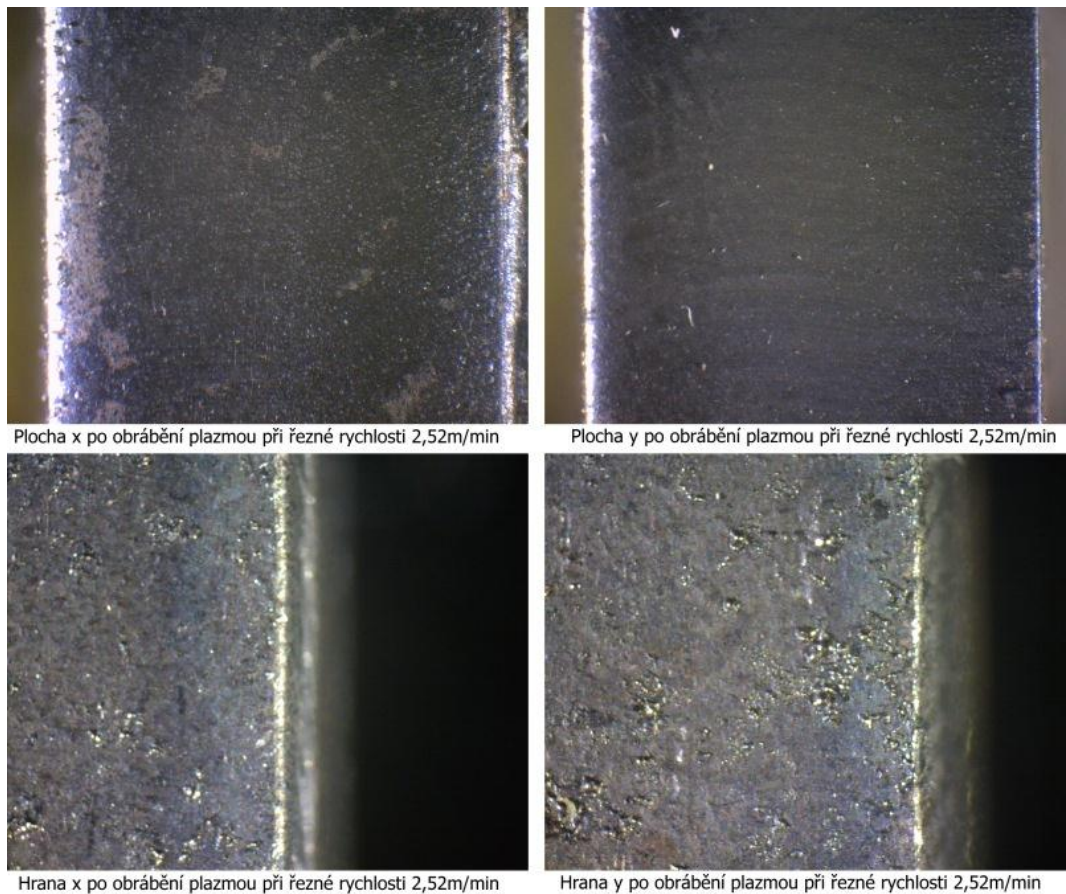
Snímky z mikroskopu vzorku 3 obráběného plazmou - materiál 11 375
